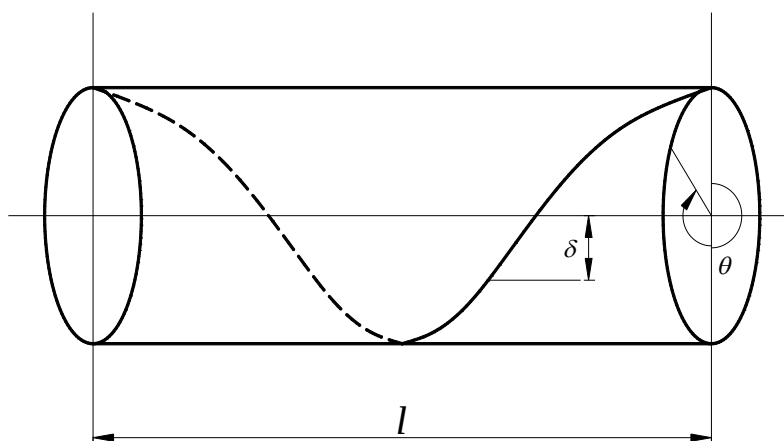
Схема скручування заготовки, що прокатана в косовалковому стані
